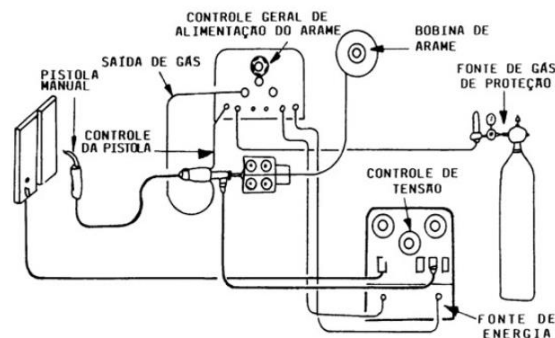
Circuito do processo de soldadura MIG-MAG [28]
